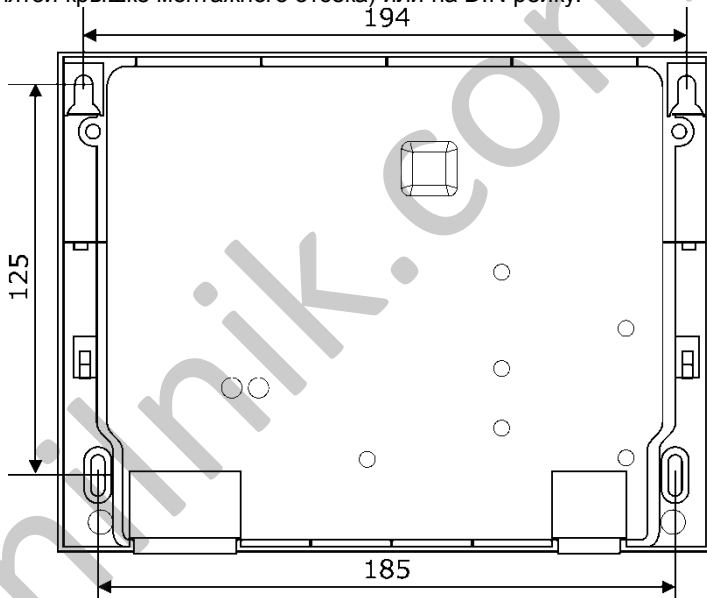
Схема крепления корпуса МВТ-2М нк
